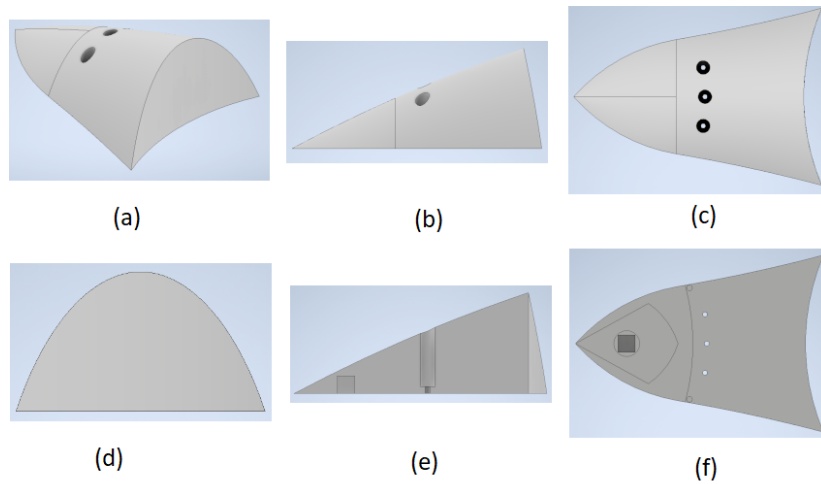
Pieza primer eslabón. (a) General, (b) Superior, (c) Frontal, (d) Derecha, (e) Inferior, (f) Frontal seccionado
